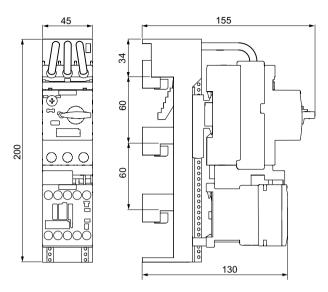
Arrancador directo S00, AC/DC, bornes de tornillo 3RA2110-..D
